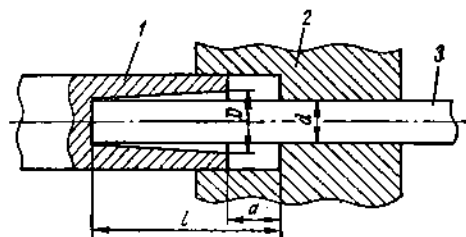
Схема конструкции штампа при наборе металла в полости пуансона:
